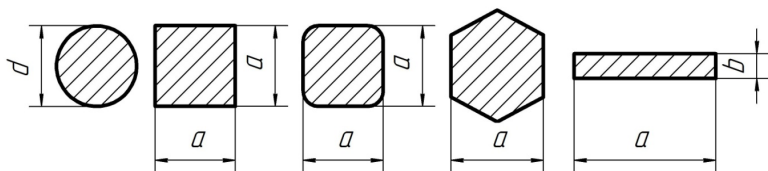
Примеры сортовой стали общего назначения с простой геометрической формой
